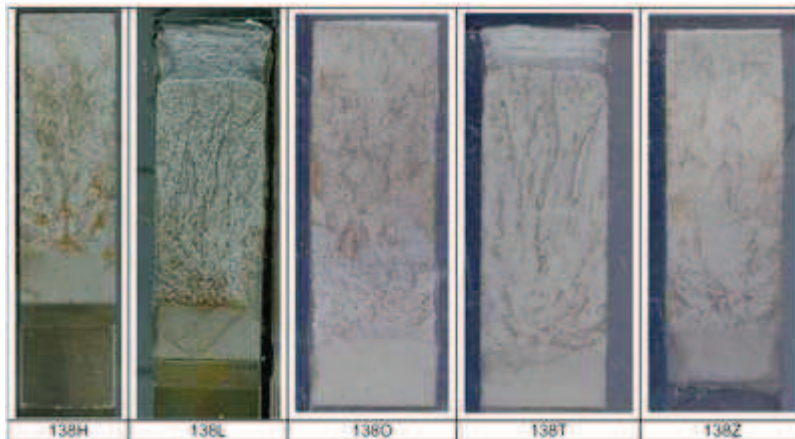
Macrographies des faciès de rupture - éprouvettes CT testées à -125°C
